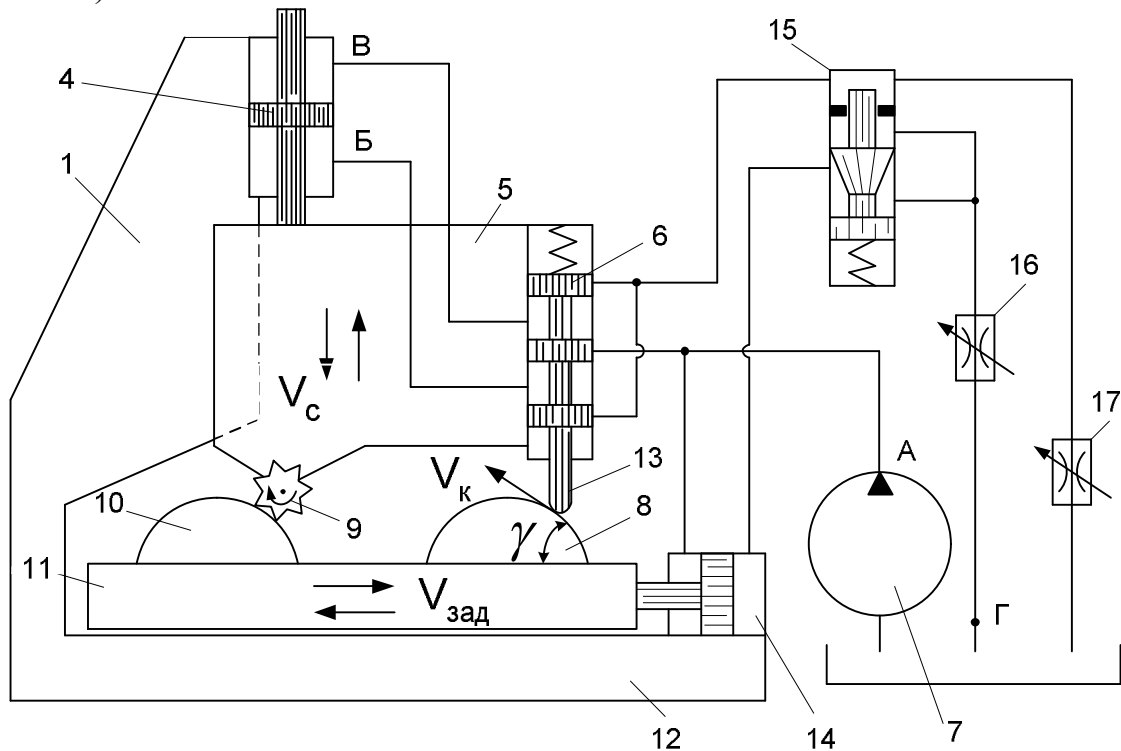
Однокоординатний однокаскадний копіювальний привід безмасштабного копіювання
